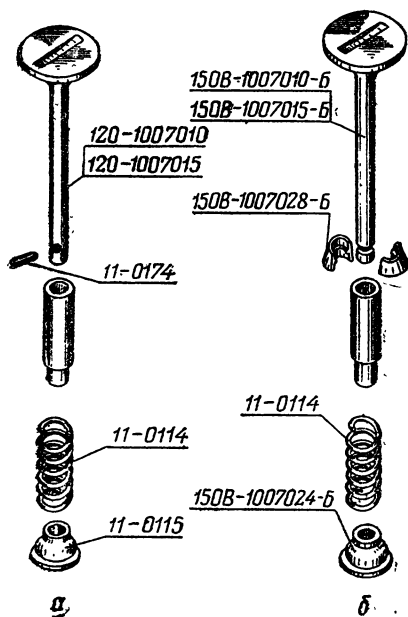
Крепление тарелки пружины: а — чекой; б — конусными сухарями
